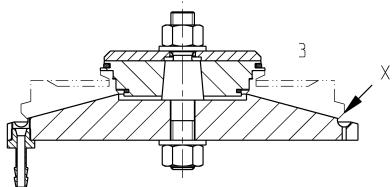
3=Schweißvorrichtung / X=1. Schweißung
